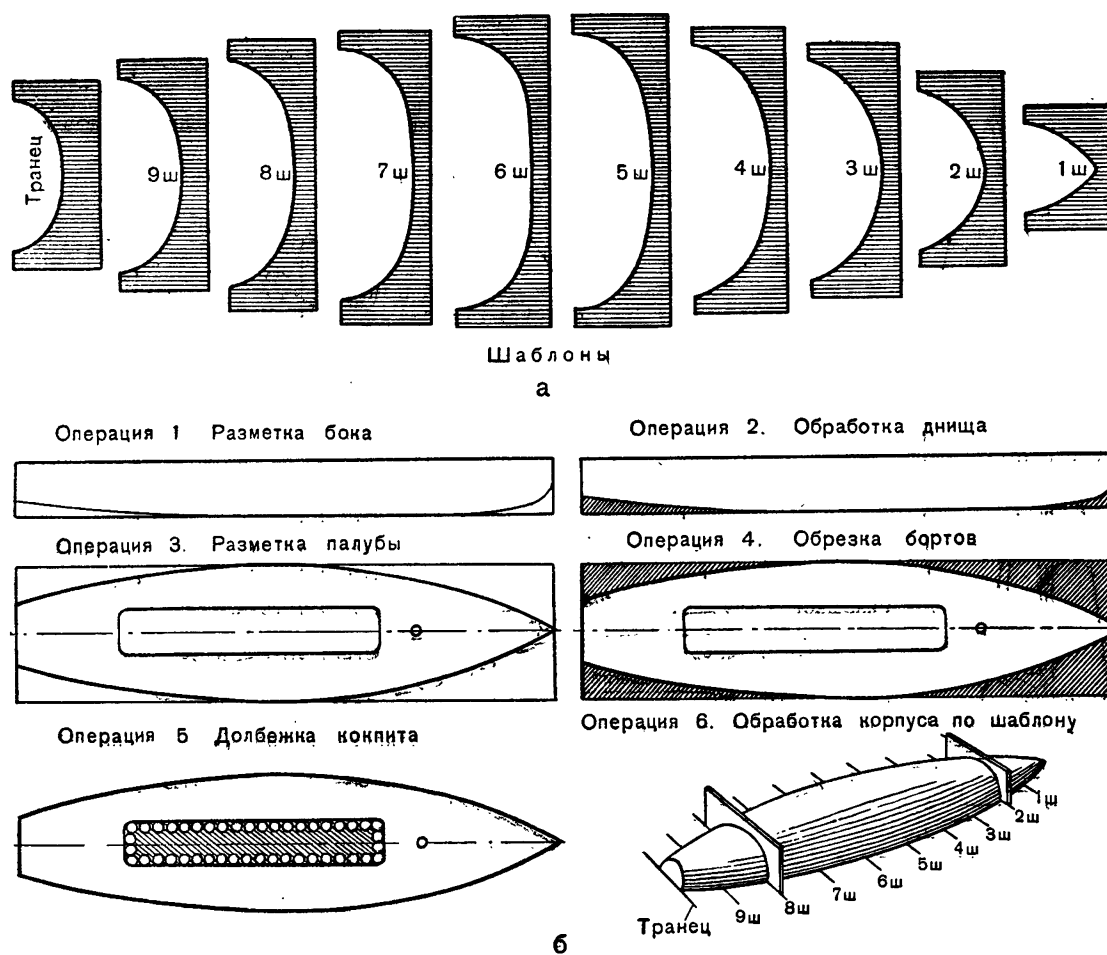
Последовательность изготовления корпуса модели швертбота.
